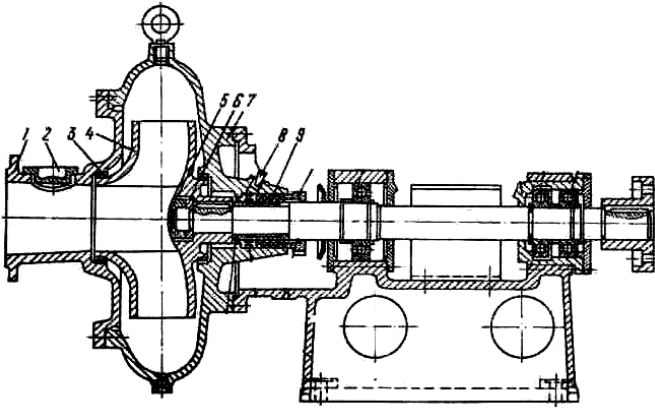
Насос типу СМ: 1 – всмоктувальний патрубок; 2 – люк прочистки насоса; 3 – ущільнення робочого колеса; 4 – робоче колесо; 5 – контргайка; 6 – гайка; 7 – корпус; 8 – підвід рідини для ущільнення; 9 – ущільнення вала
